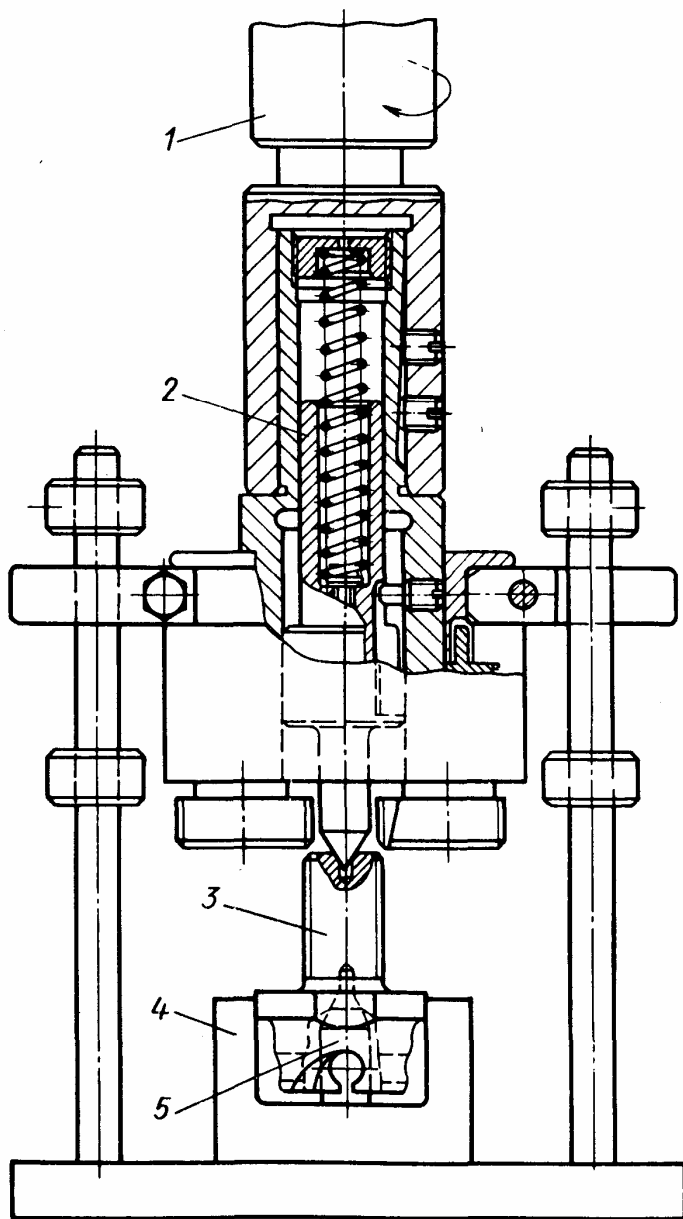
Схема нарізання зовнішньої різьби головкою з пружинним центром: 1 – шпиндель верстата; 2 – пружинний центр; 3 – заготовка; 4 – пристосування; 5 – нижній центр
